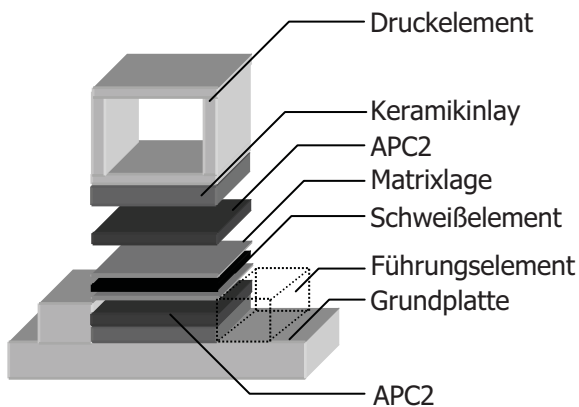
Explosionszeichnung des APC2-Werkzeuges
